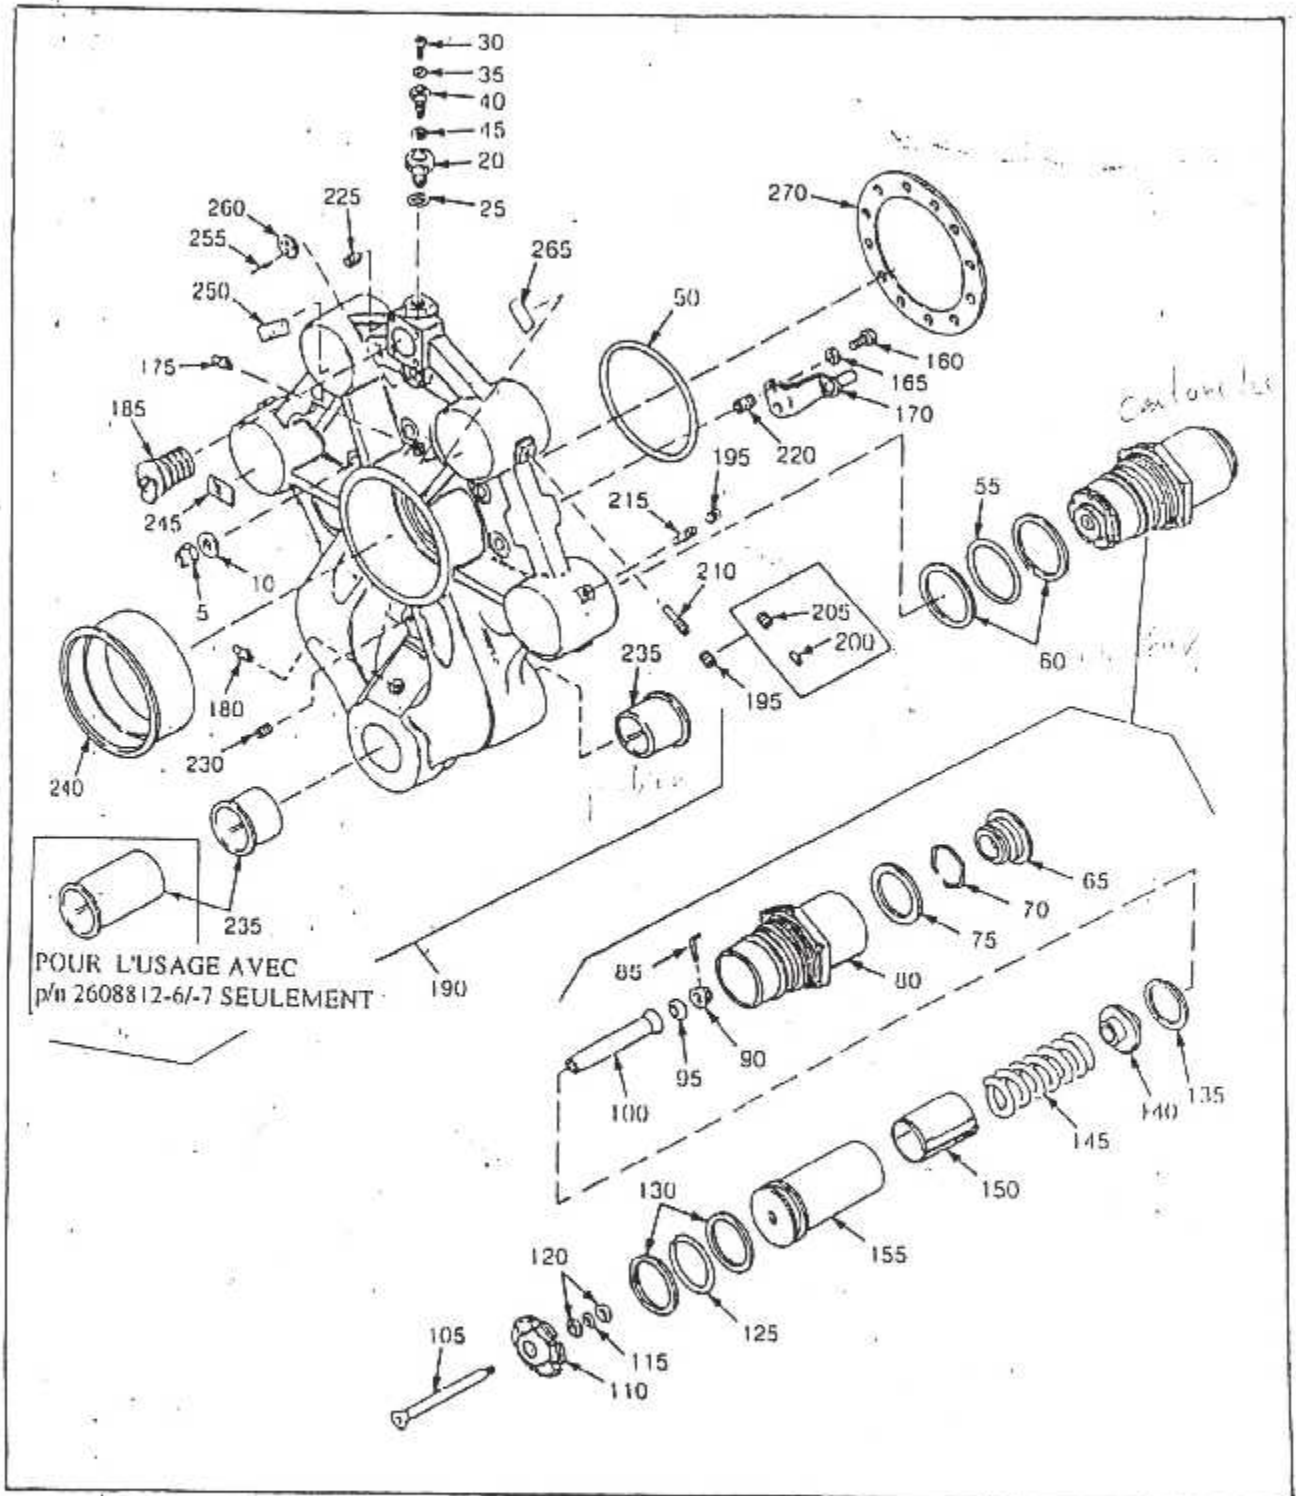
Vue éclatée de carter du bloc de frein
